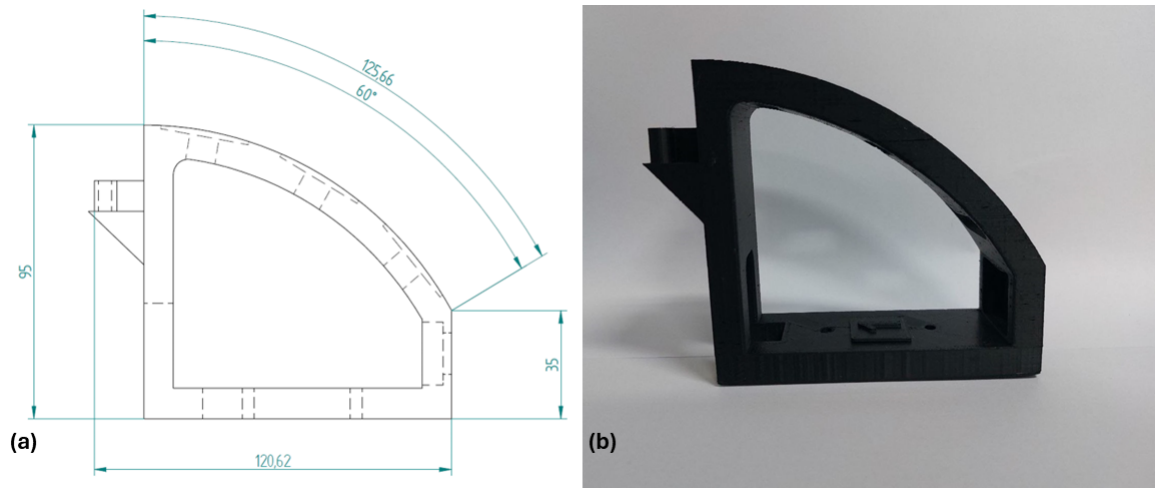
Vista lateral do *rib*: (a) Desenho técnico (b) Peça impressa.
